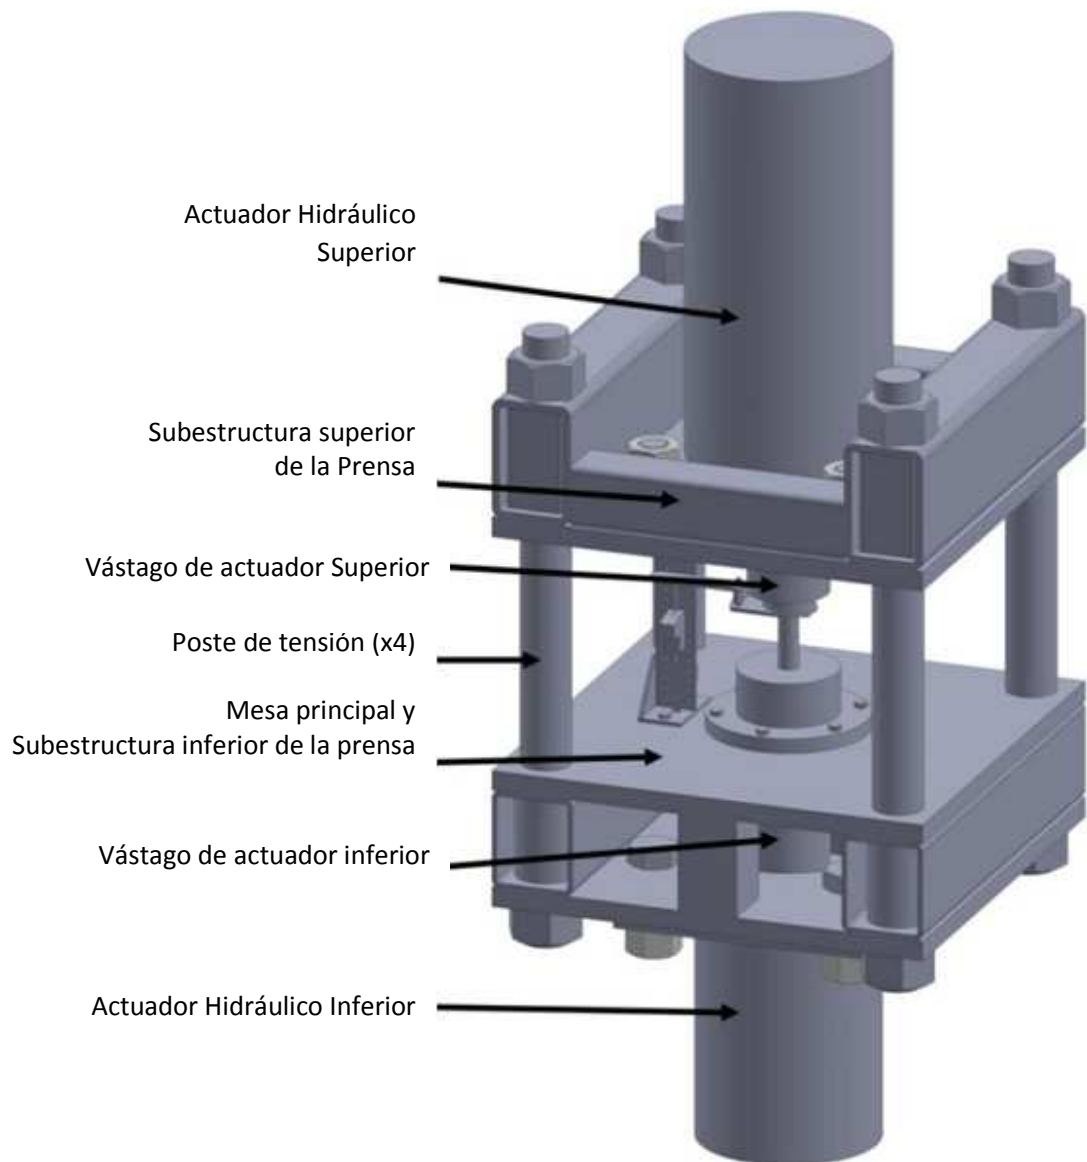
Modelo CAD de prensa y conjunto principal de su estructura.
